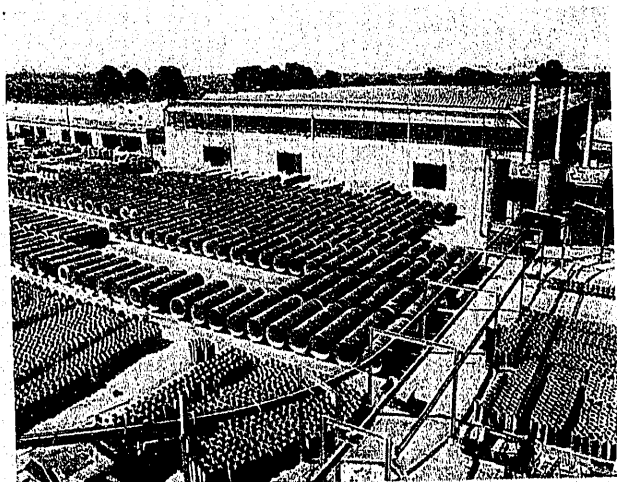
^a. — Acopio de tubos de hormigón en la N. V. Betondak de Arkel.
